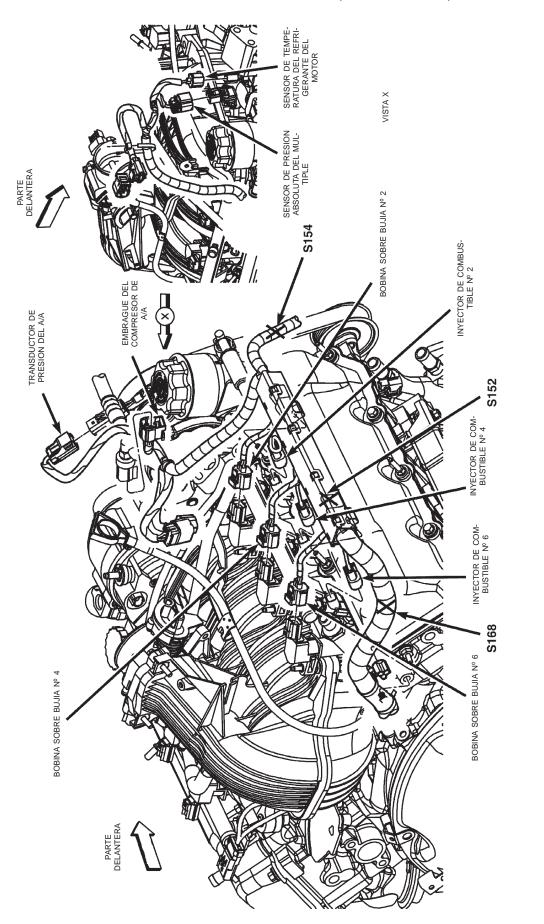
LADO DERECHO DEL MOTOR 3.7L
